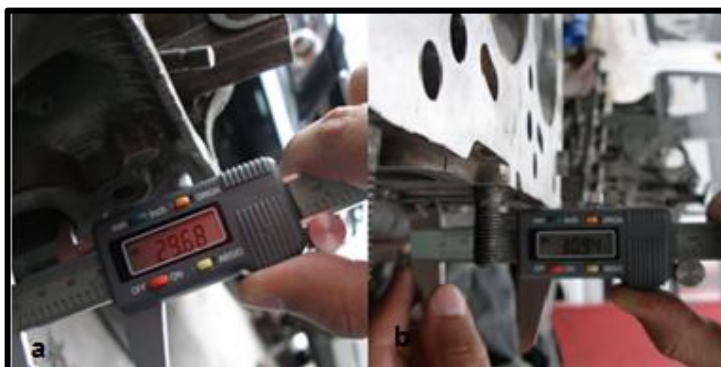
a): Conducto de Escape Original 2.13 b): Conducto de Escape Modificado.
